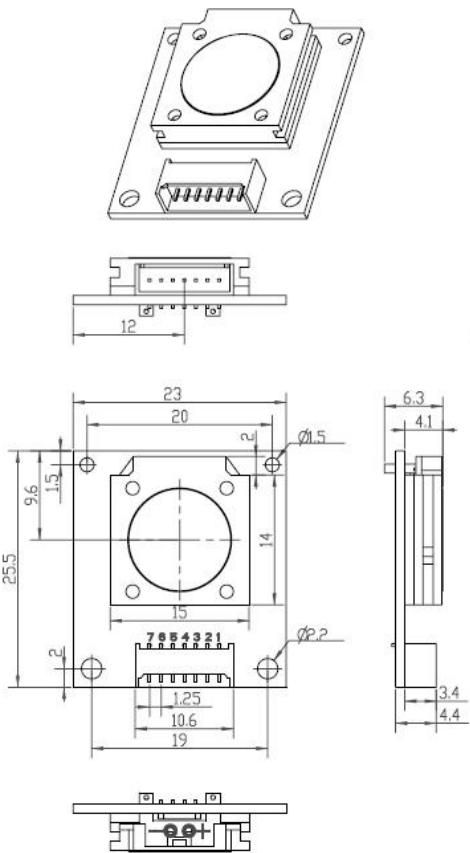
： 模组结构图 (模组尺寸公差±0.2mm)
